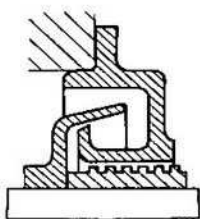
Empaquetadura combinada: disco deflector, rosca de retorno
